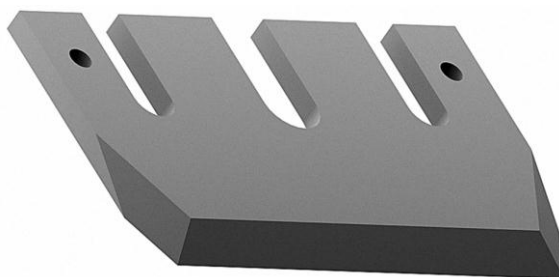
Режущий инструмент малоножевой торцово-конической фрезы
